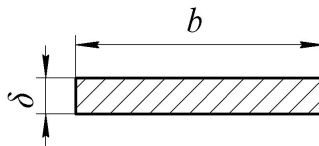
Форма та розміри поперечного перерізу пружини
